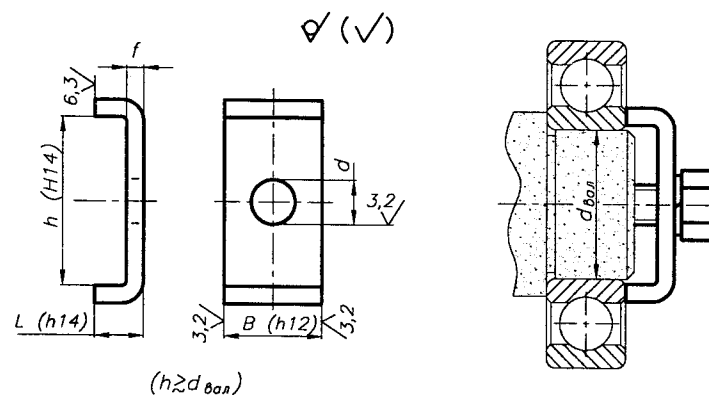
Конструкция и размеры стопорных скоб
